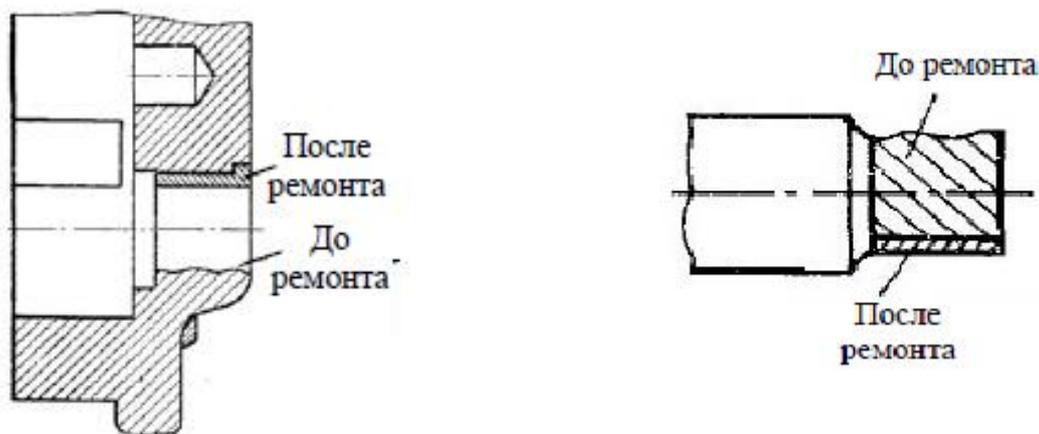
Схема установки втулки подшипника в изношенном корпусе
